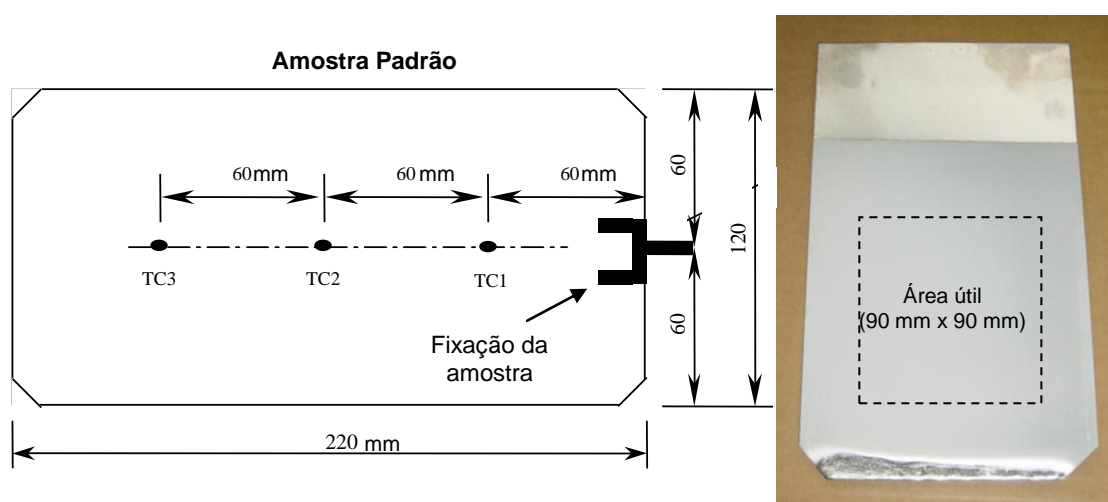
Desenho esquemático do corpo de prova utilizado no equipamento HDPS, com detalhes do local de soldagem dos termopares.
